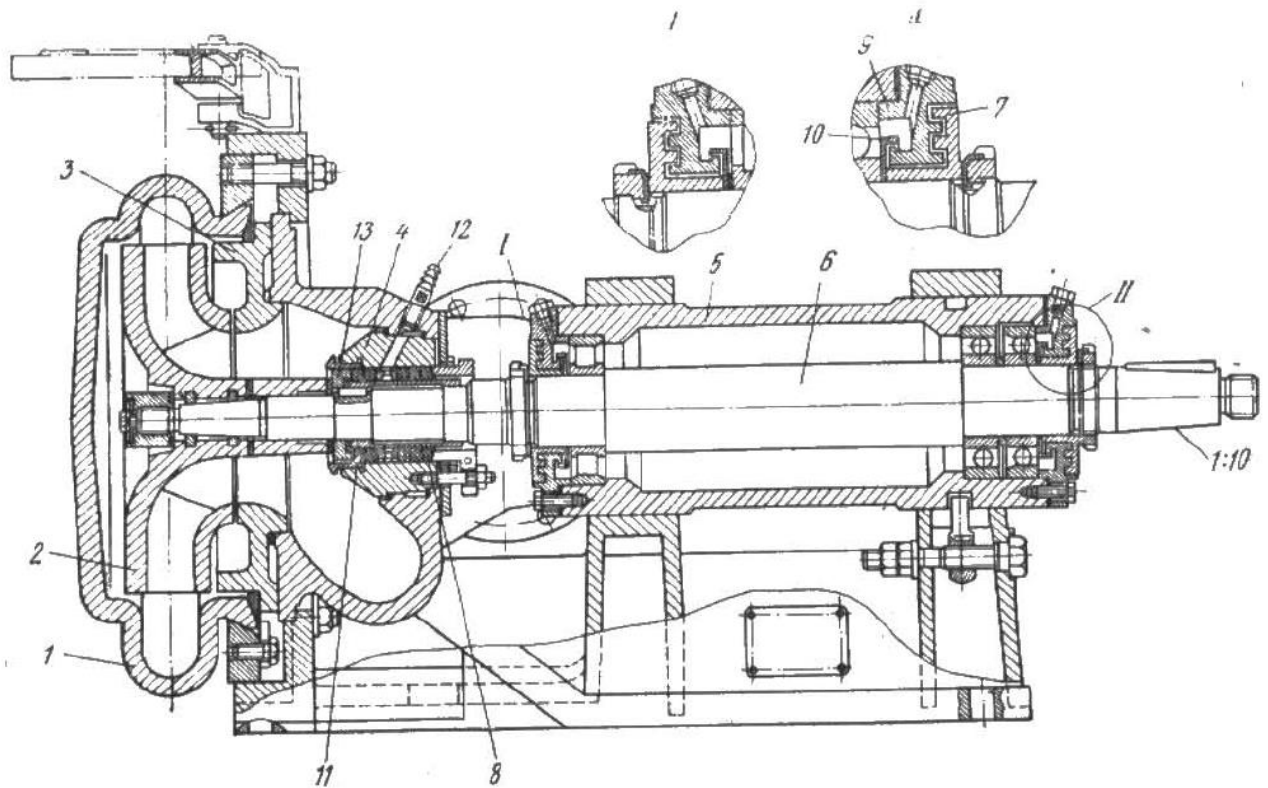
Насос пісковий 6Пс-10 [8]: 1 - уліта; 2 - робоче колесо; 3 - диск; 4 - корпус сальника; 5 - склянка; 6 - вал; 7 - кришка лабіринту; 8 - набивання сальника; 9 - кришка притискна; 10 - кільце відбивне; 11 - втулка захисна; 12 - ніпель подачі води в сальник; 13 - кільце сальника
